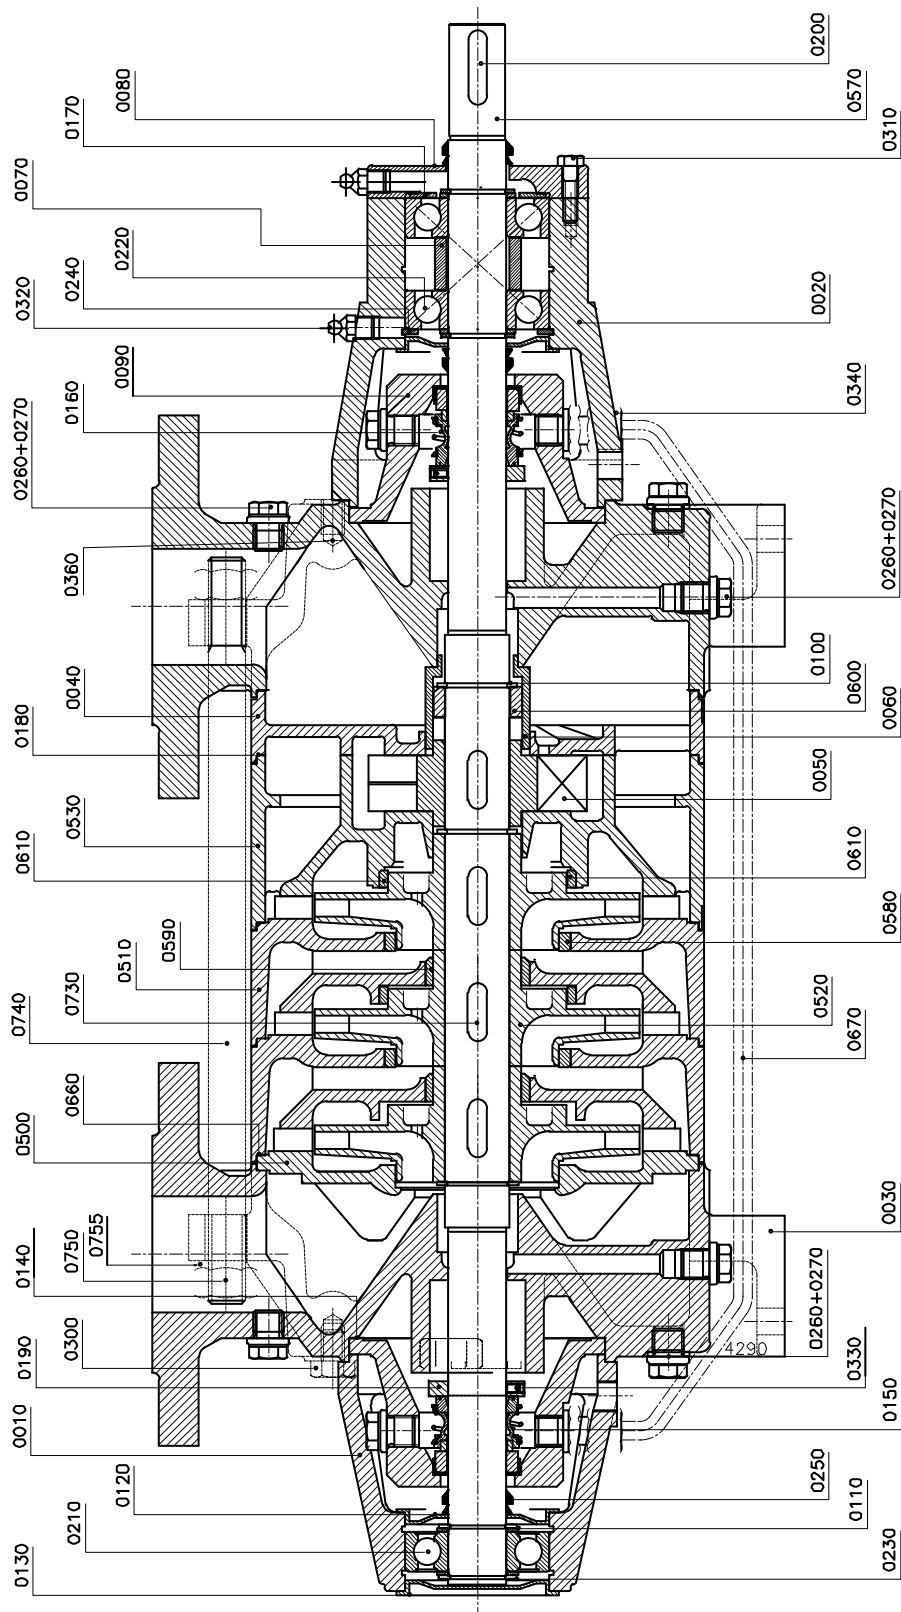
MCHZ 14a/b med tung lagerkonstruksjon.
